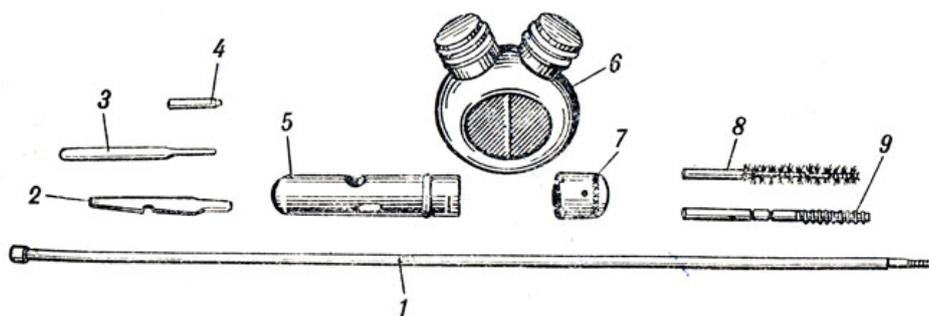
Принадлежность: 1 – шомпол; 2 – отвертка; 3 – выколотка; 4 – шпилька; 5 – пенал; 6 – масленка; 7 – крышка; 8 – ершик; 9 – протирка.
